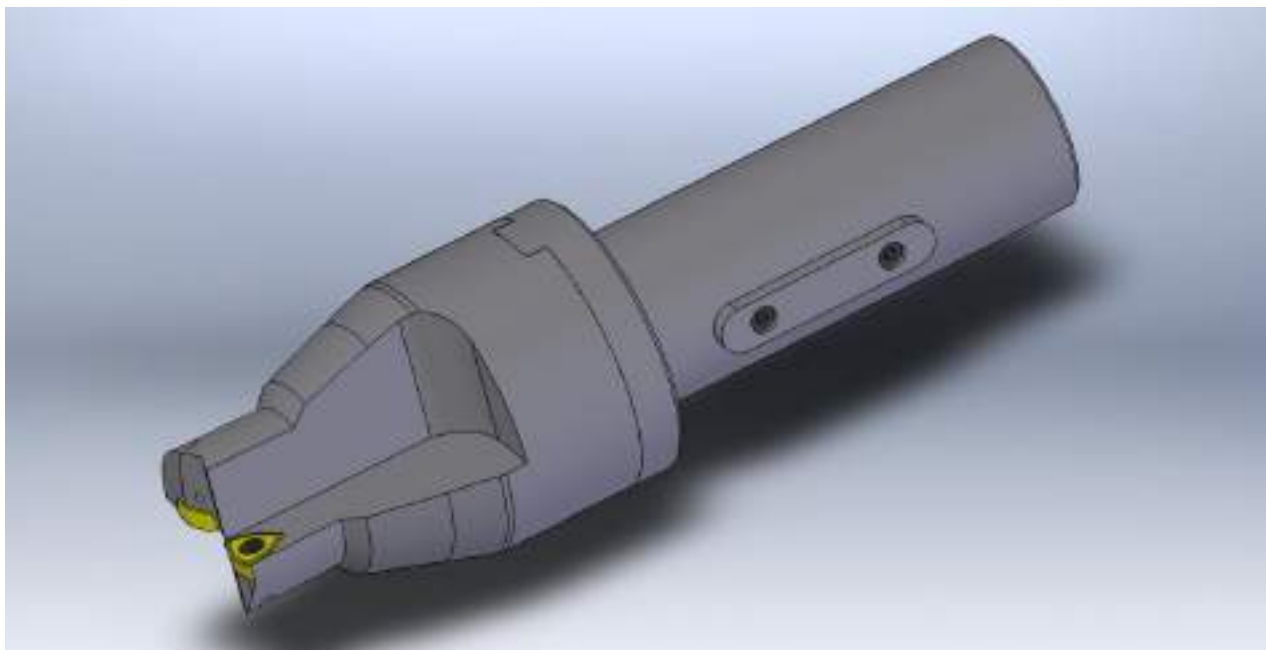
Загальний вид свердла (Solid Works)
